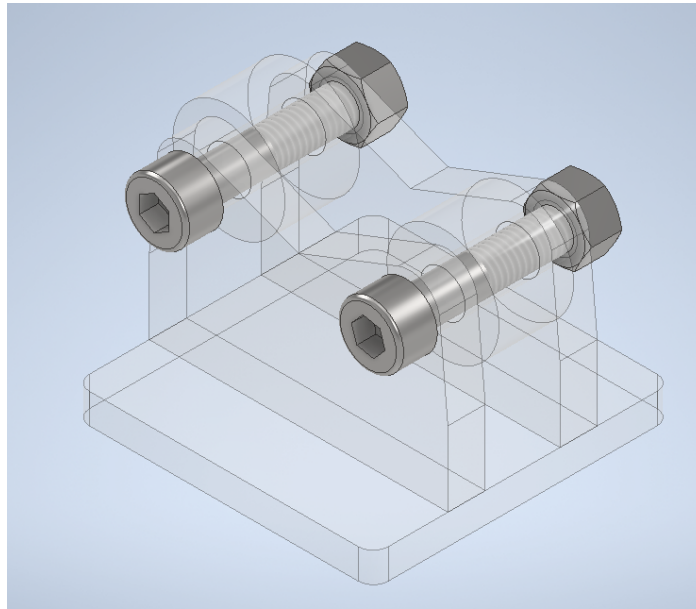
Modelado 3D del conjunto ruedas de apoyo.
